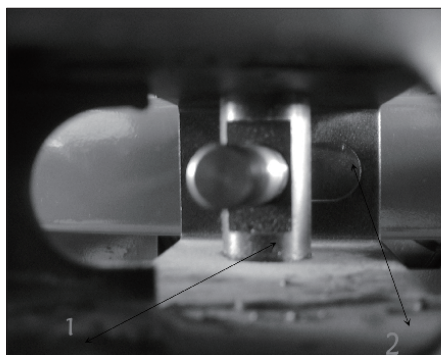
Вставьте рычаг лопатки отрыва шины [1] в опорную плиту рычага лопатки отрыва шины на коробке, чтобы совместить два отверстия, установите болты (Рис. 4-5-3) и затяните гайки (Рис. 4-5-4), подвесьте пружину растяжения (Рисунок 4-6-3).
